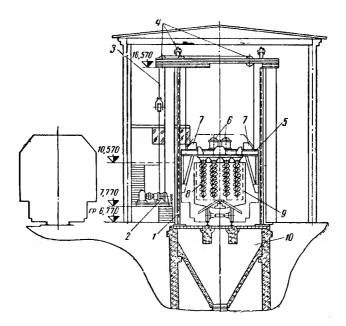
Бурофрезерная рыхлительная машина 1— направляющие каретки портала; 2— лебедка подъема каретки; 3— трос; 4— блоки; 5— каретка; 6— электродвигатели привода бурофрезерных барабанов; 7— электродвигатели привода бокового перемещения рыхлителя; 8— бурофрезерные барабаны; 9— боковые стенки кузова гондолы; 10— приемный бункер
